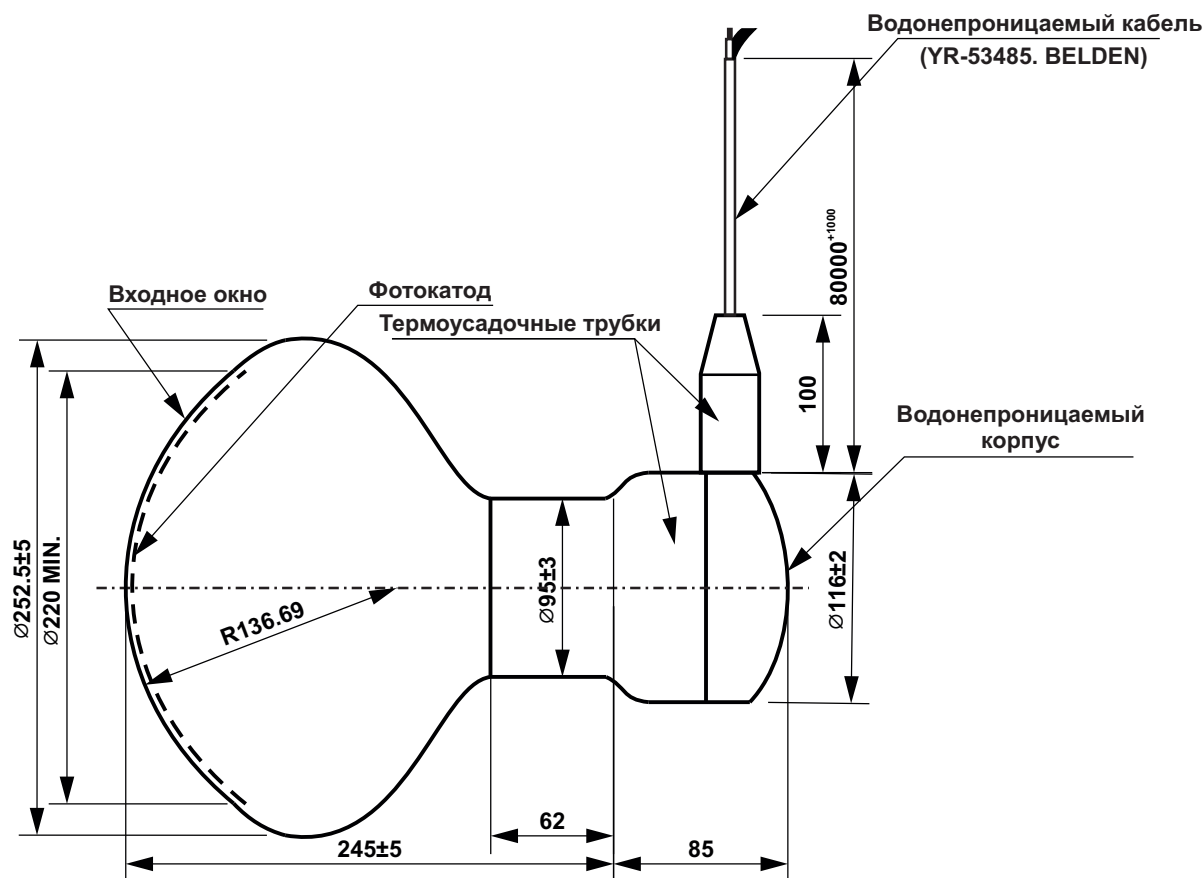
Габаритный чертёж фотоумножителей Hamamatsu R7081-100 WA-S70.
